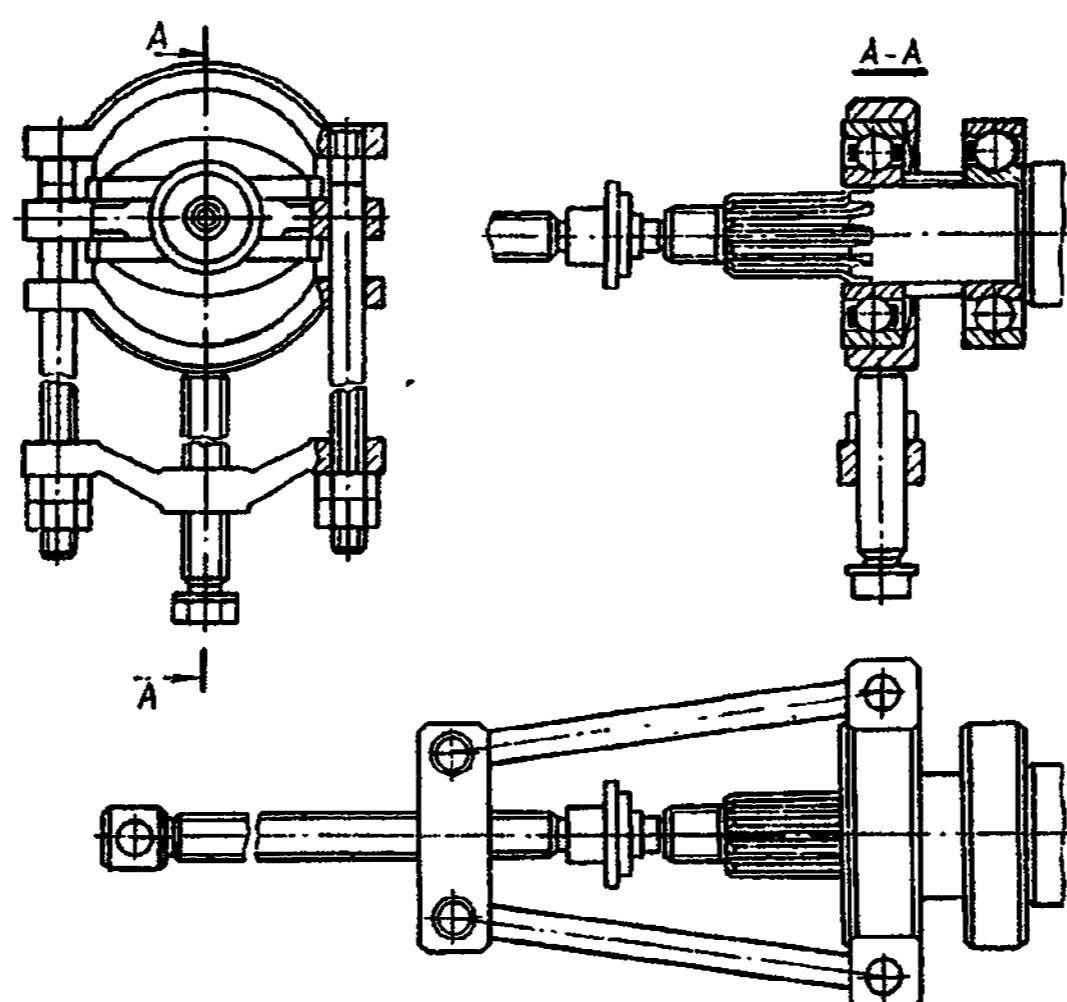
Снятие подшипников вала привода коробки отбора мощности
